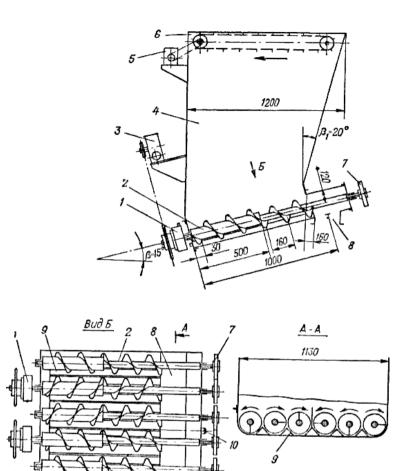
Шнековый дозатор ДС-15 (тип I): I — электромагнитная муфта; 2 — шнек; 3 — редуктор; 4 — бункер; 5 — редуктор транспортёра-выравнивателя; 6 — транспортёр-выравниватель; 7 — шестерня; 8 — выгрузное окно; 9 — перегородка; 10 — пробка сливного отверстия
